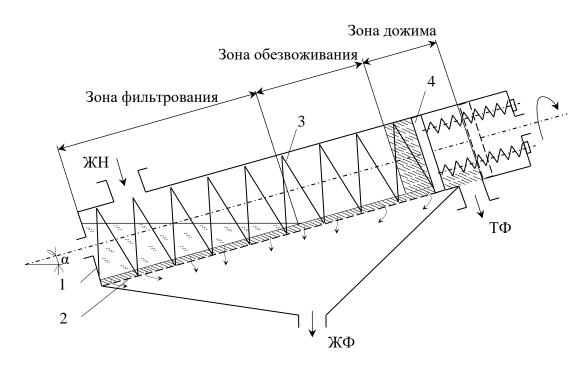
Схема конструкции щеточного шнека: 1-корпус шнека; 2-перфорированный желоб U-образной формы; 3- шнек; 4-дожимное устройство
